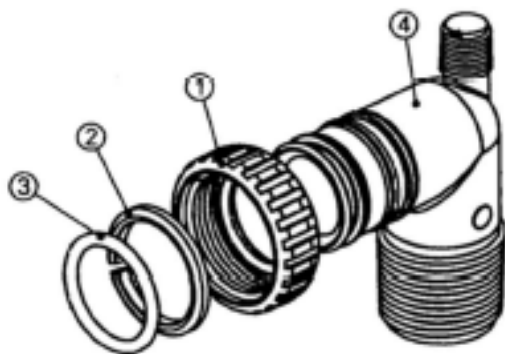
1"- Резьбовое колено 90° (ПВХ)
